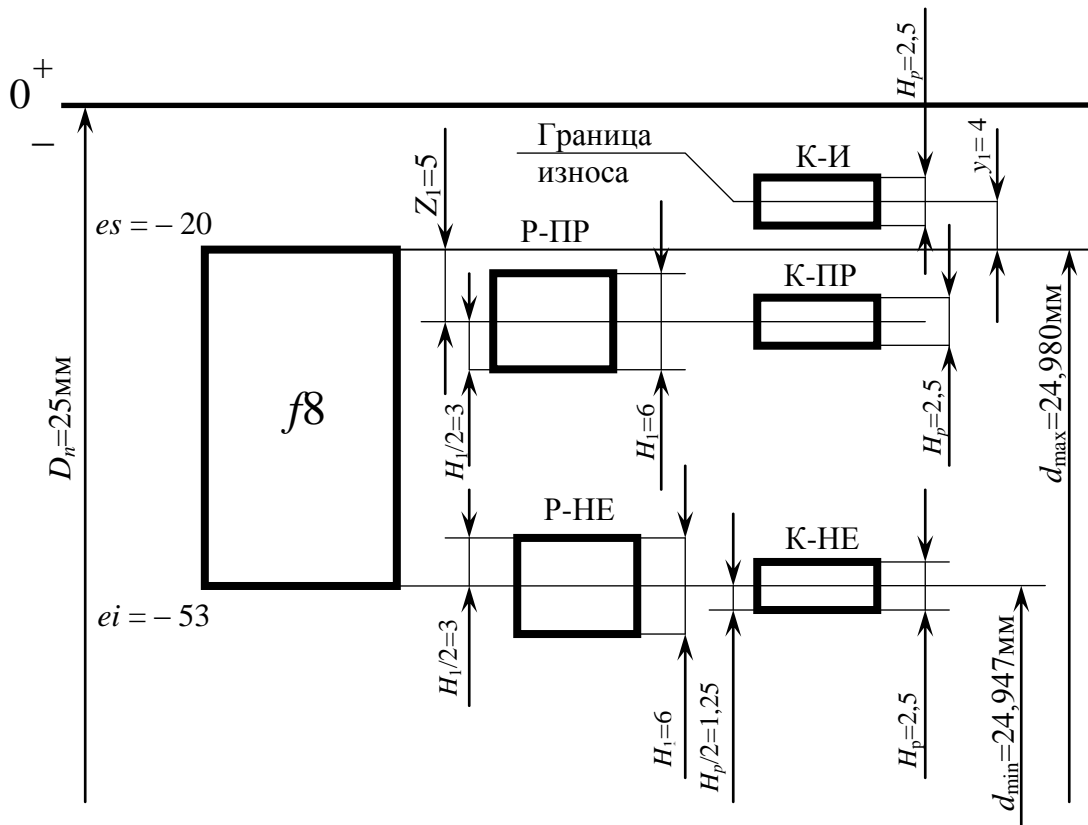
Схема расположения полей допусков вала $\text{Ø}25f8$, рабочих и контрольных калибров
